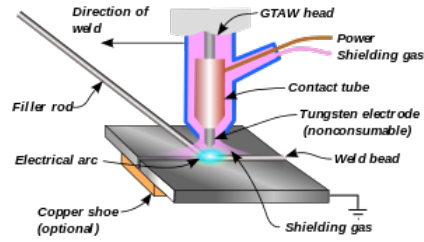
Diagrama de equipo de soldadura TIG
